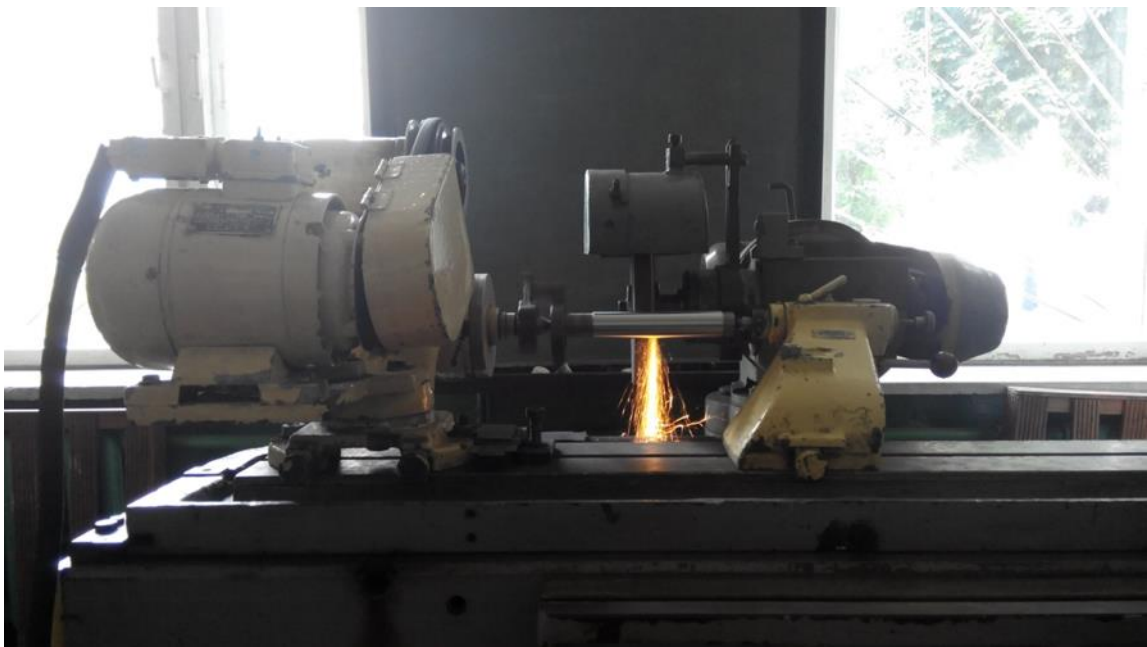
Процес шліфування циліндричної поверхні вала периферією орієнтованого круга
